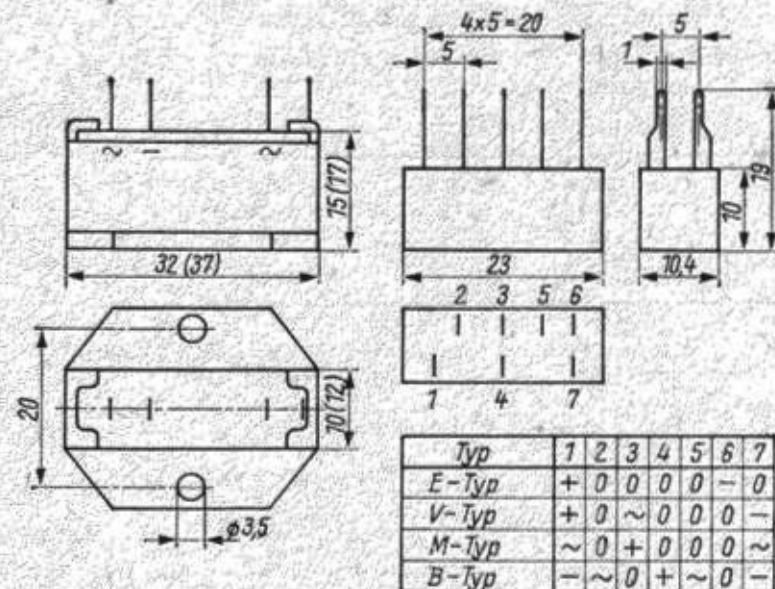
Bauformen der Selenblockgleichrichter im Metallgehäuse (links) und im Plastikgehäuse (rechts)
